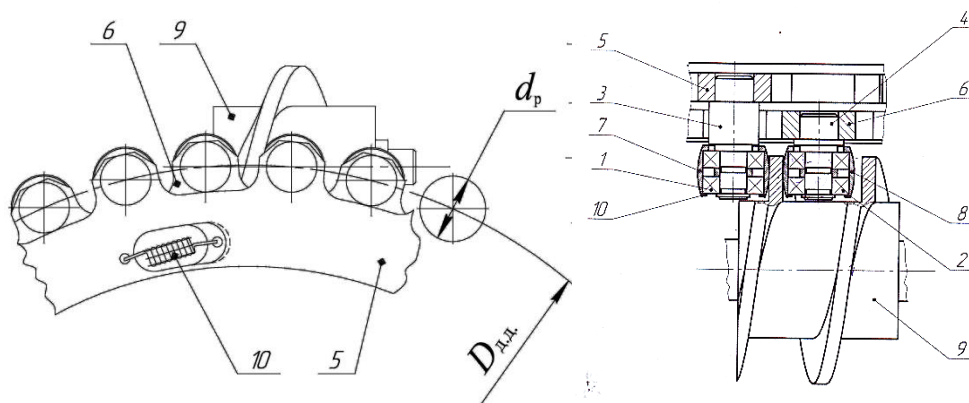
Червячно-роликовая передача: 1,2) 2 шарикоподшипник; 3,4) стойка; 5) вспомогательный диск; 6) основной диск; 7,8) ролик; 9) червяк; 10) пружина. d_p – диаметр ролика, $D_{д.д.}$ – диаметр диска, на котором расположены ролики
